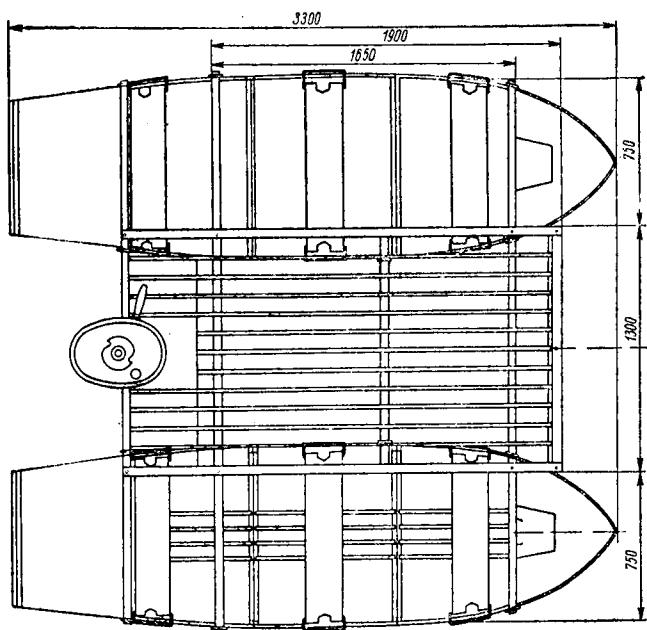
Разборная двухкорпусная дача «Ладога» ДБ (вид сверху). Длина средней палатки 1,9, ширина 1,3 м. Длина боковой палатки 1,65, ширина 0,75 м.
